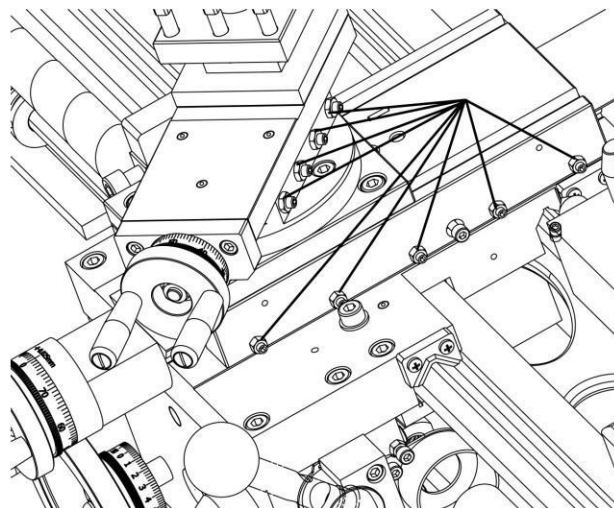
Винты направляющих поперечного и крестового суппортов.
